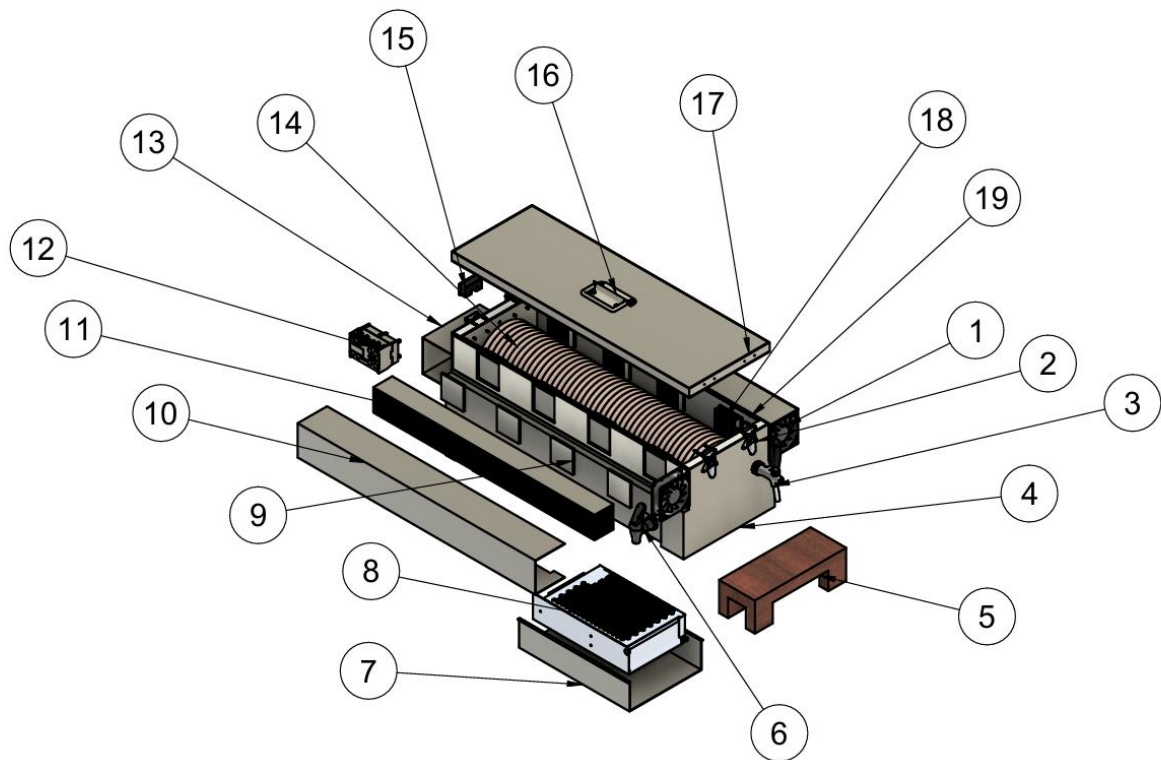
Vista explodida protótipo da máquina de arrefecimento; Fonte:(Autor, 2025)
